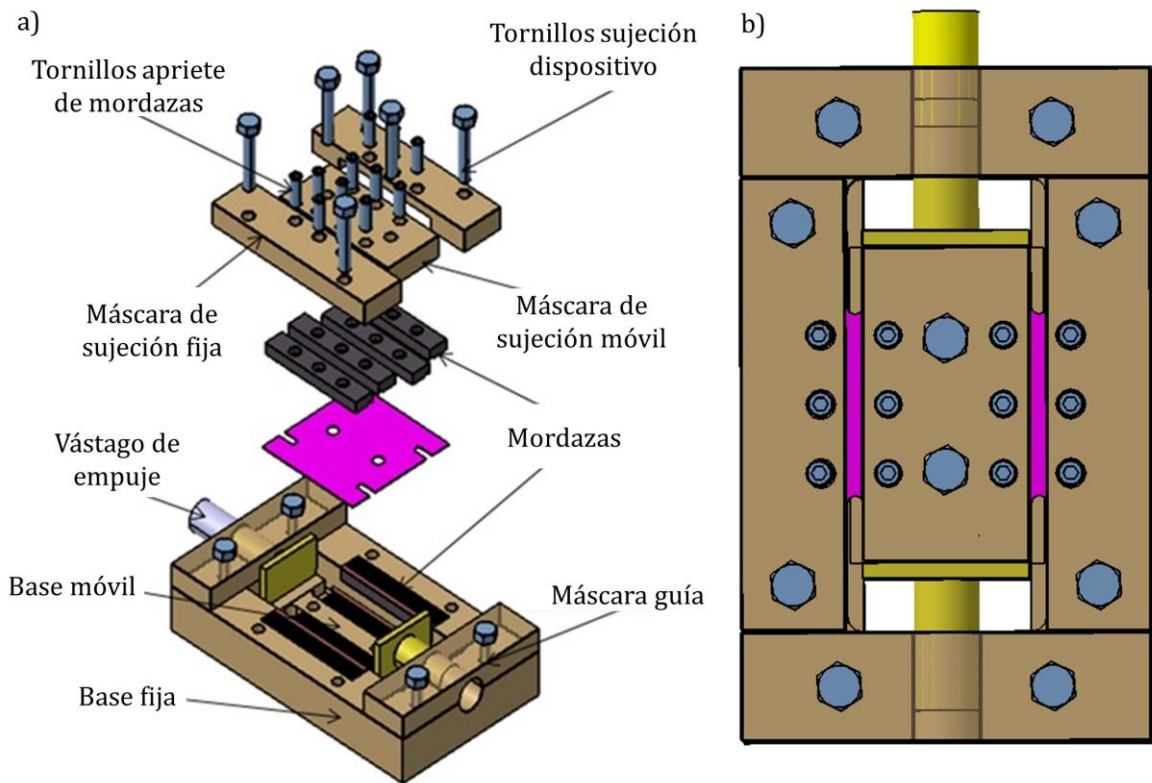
a) despiece y b) conjunto armado del dispositivo de corte simple diseñado basado en Miyauchi
